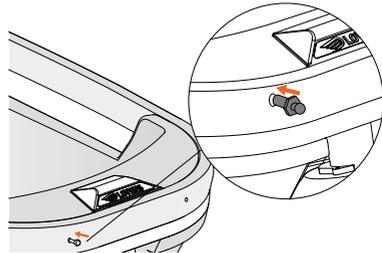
Befestigen des Bolzens mit Druckanschluss.
